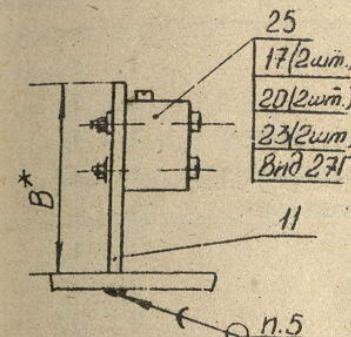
Пример установки подстроечных реистров R1...R5 на печатную плату. Согласно спецификации на сборочный узел поз. 11 - стойка, поз.17 - винт, поз. 20 - шайба, поз.23 - гайка , поз. 25 - резистор.
